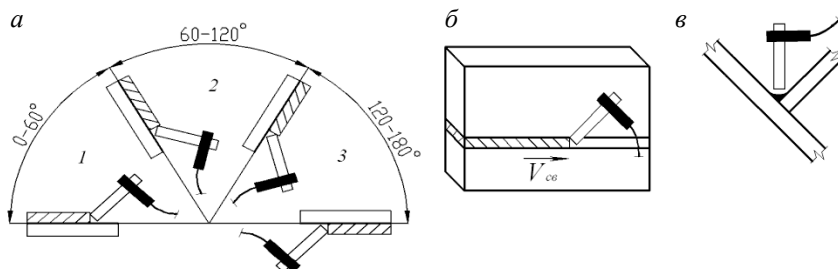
Положение сварных швов в пространстве:
